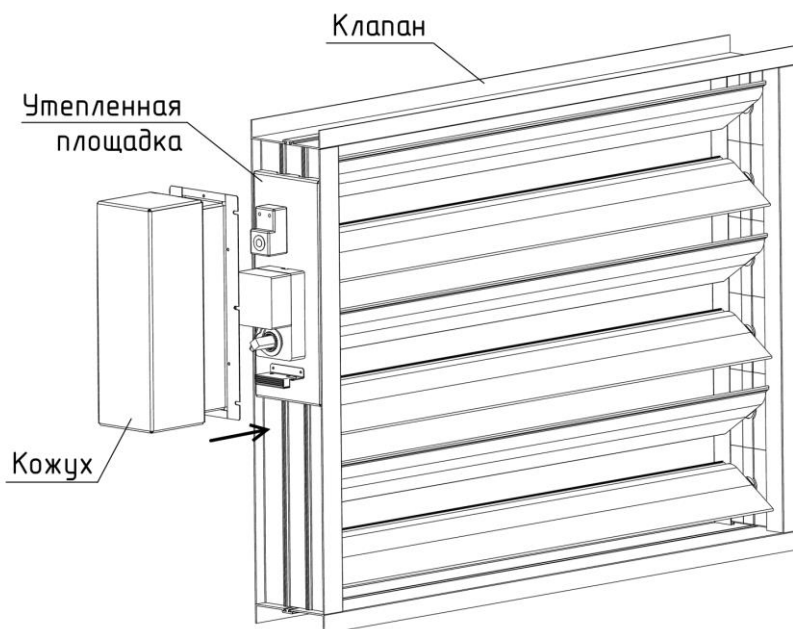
Установка обогреваемого кожуха непосредственно на клапан
